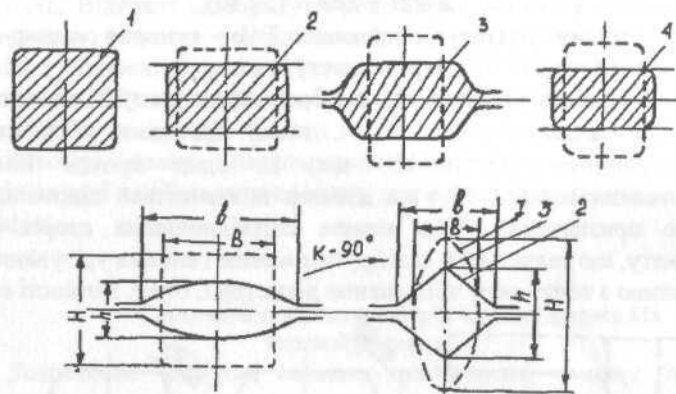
Система прямокутник - гладка бочка (1-заготовка; 2-гладка бочка; 3-ящичний калібр; 4-гладка бочка)
